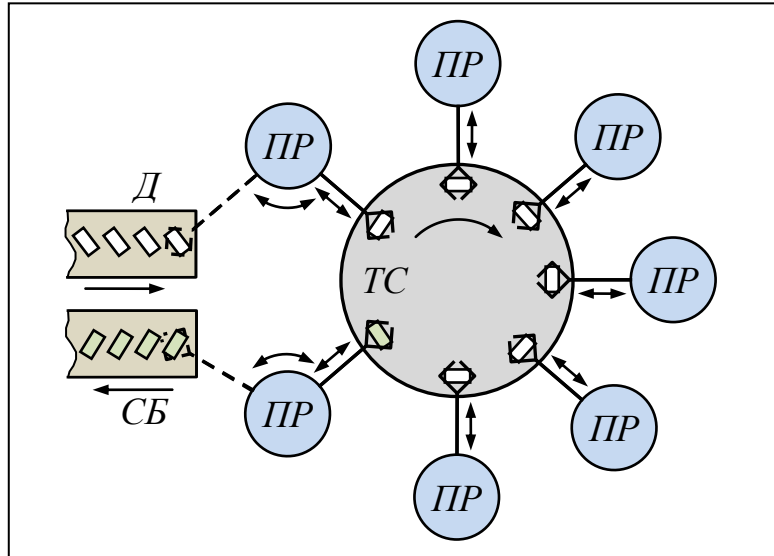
Схема сборочного РТК с круговой компоновкой
